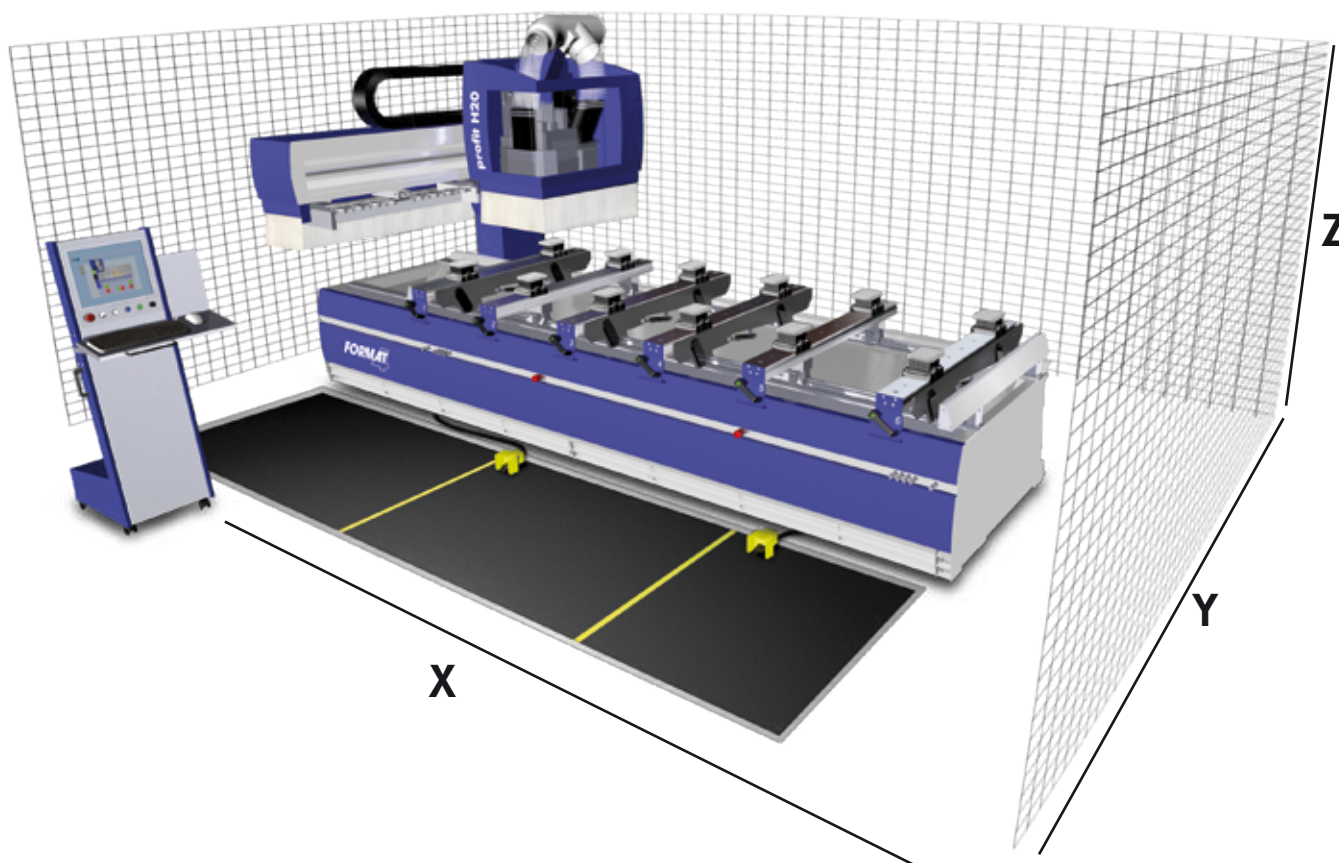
Размеры и масса станка (включая распределительный шкаф)
